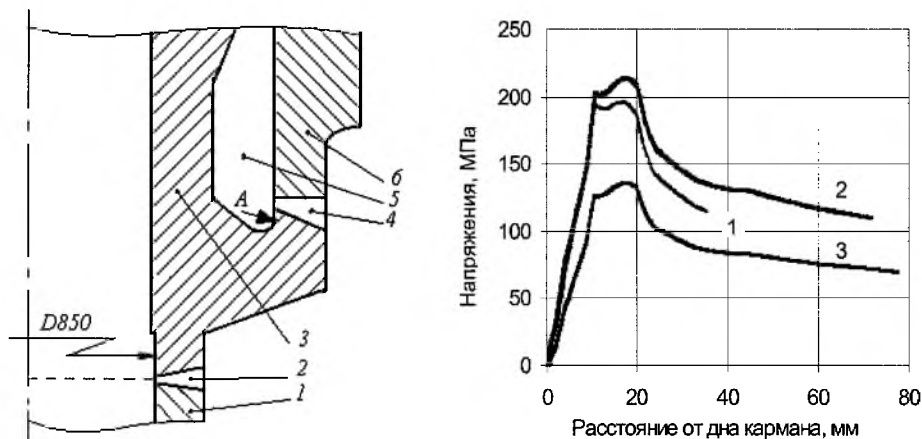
Узел приварки: 1 – главный циркуляционный трубопровод; 2, 4 – сварной шов; 3 – коллектор; 5 – карман; 6 – патрубок парогенератора; А – место инициирования разрушения.
